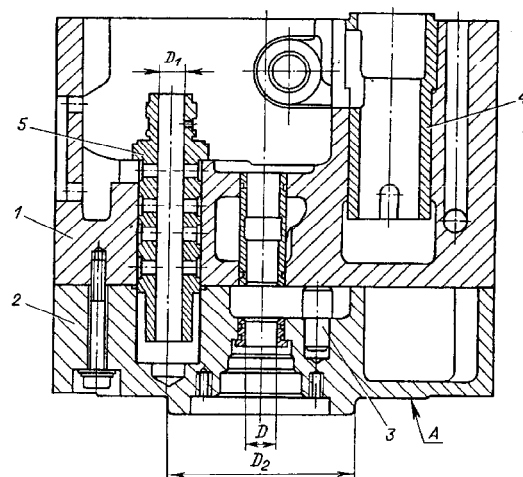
Корпусы 3 средний и нижний в сборе /рис. 116/
